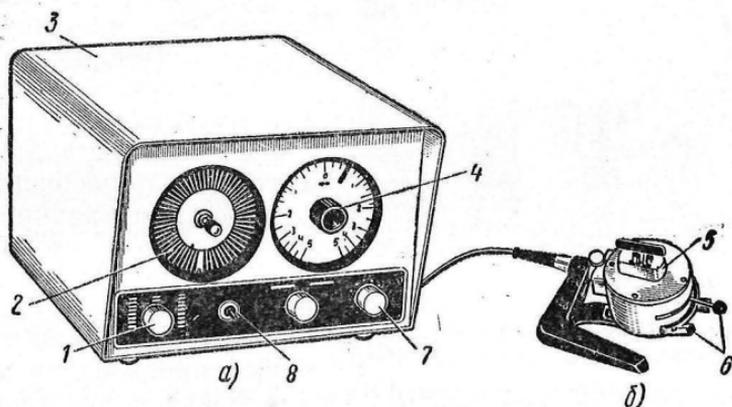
Установка для регулировки мгновенного суточного хода и одновременной установки «выкачки»:
